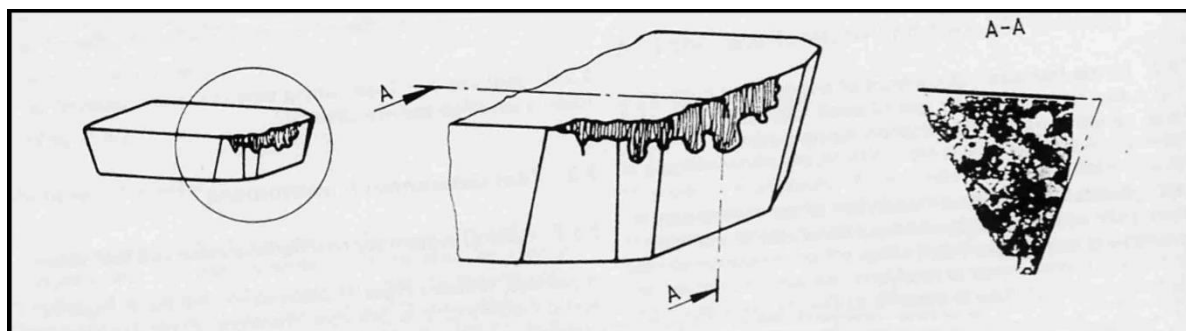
Representação do desgaste de flanco não uniforme e sua vista de corte (ISO-8688-1, 1989)
